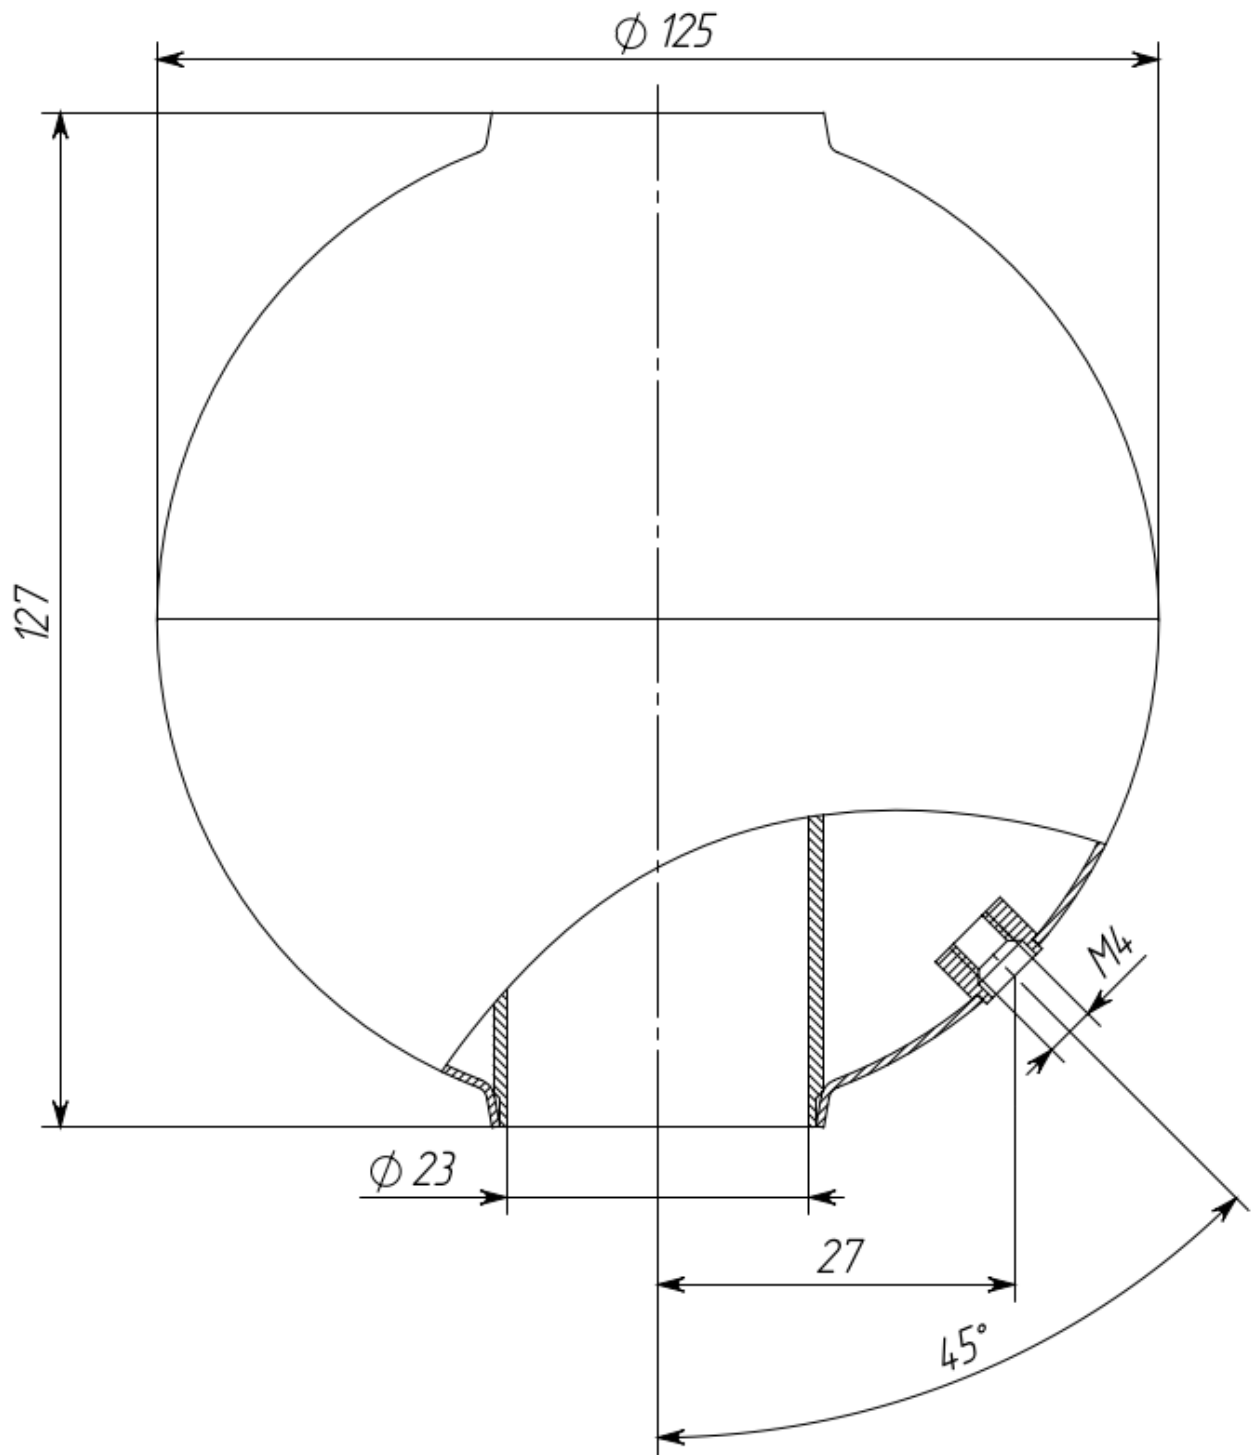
Габаритные и установочные размеры поплавок Н125 (масса 220 г)
